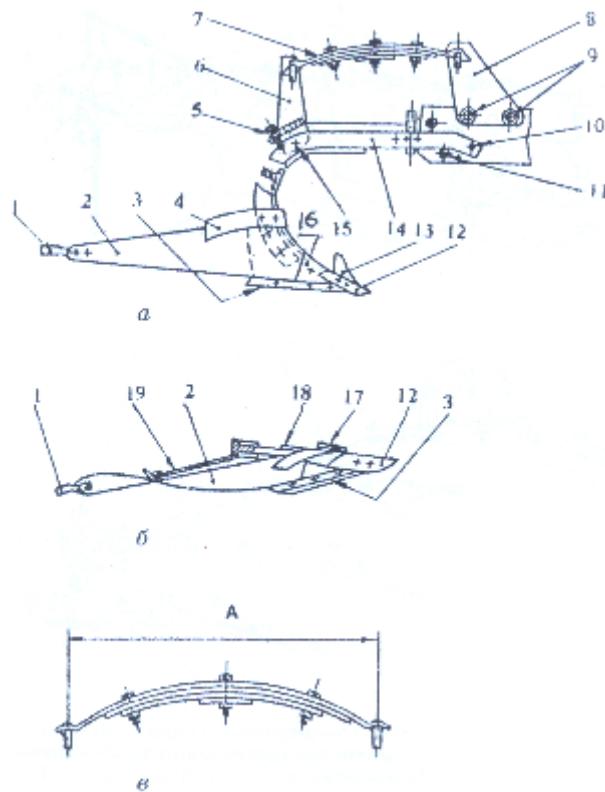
Корпус плуга с рессорным предохранителем:
